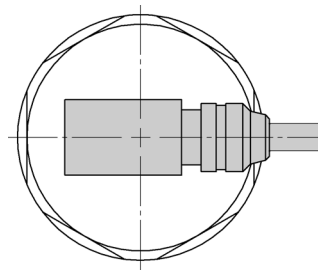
Steckverbinder BKS-S233-PU- _ _ , Abgang axial
